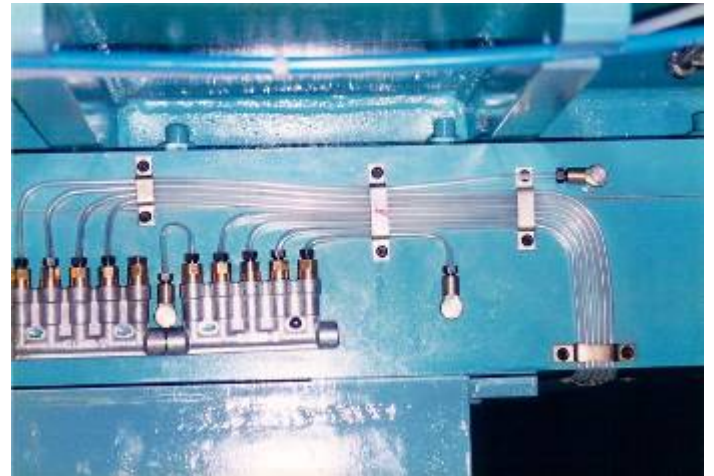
Die Schmierung. Genügend Schmierstellen für Kurzhubbewegungen. Da die Maschine viel Gewinde schneidet, oft bis zu 30 Durchgänge pro Gewinde, sind viele Schmierstellen gut für die Lebensdauer der Maschine.
